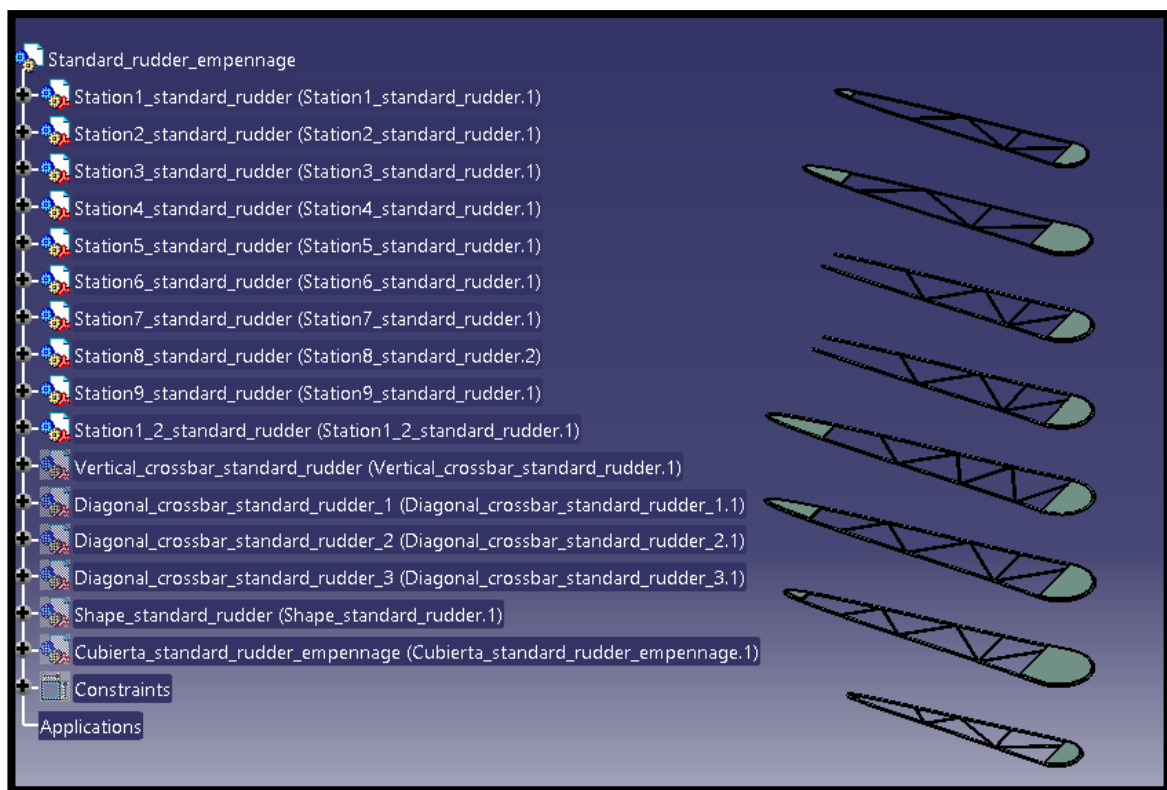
Timón de dirección: secciones convenientemente colocadas en el entorno del conjunto
